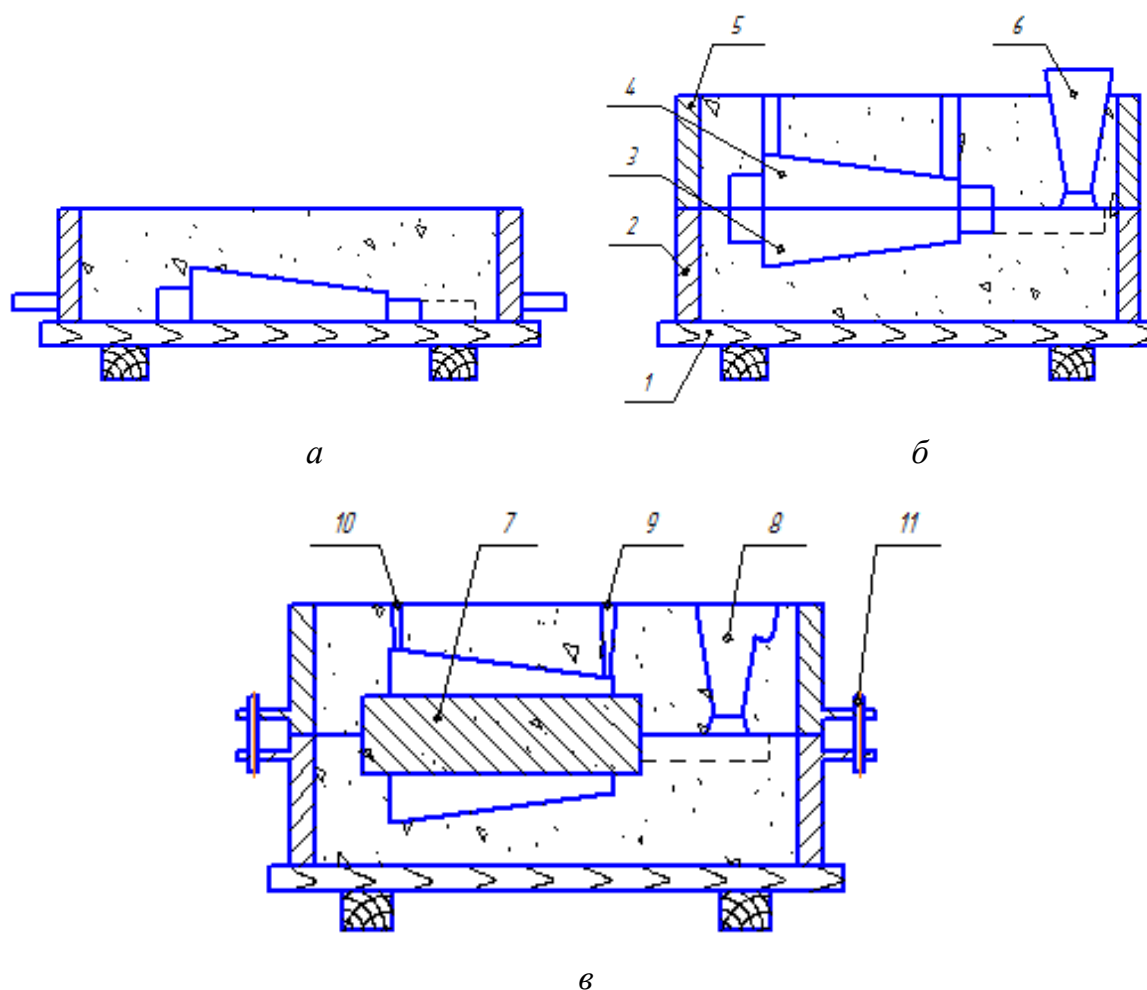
Ручная формовка в двух опоках: а – формовка нижней опоки; б – формовка верхней опоки; в – форма в сборе: 1 – подмодельная доска; 2 – нижняя опока; 3 – нижняя половина модели; 4 – верхняя половина модели; 5 – верхняя опока; 6 – модель стояка; 7 – стержень; 8 – литниковая система; 9 – выпор; 10 – прибыль; 11 – штырь
